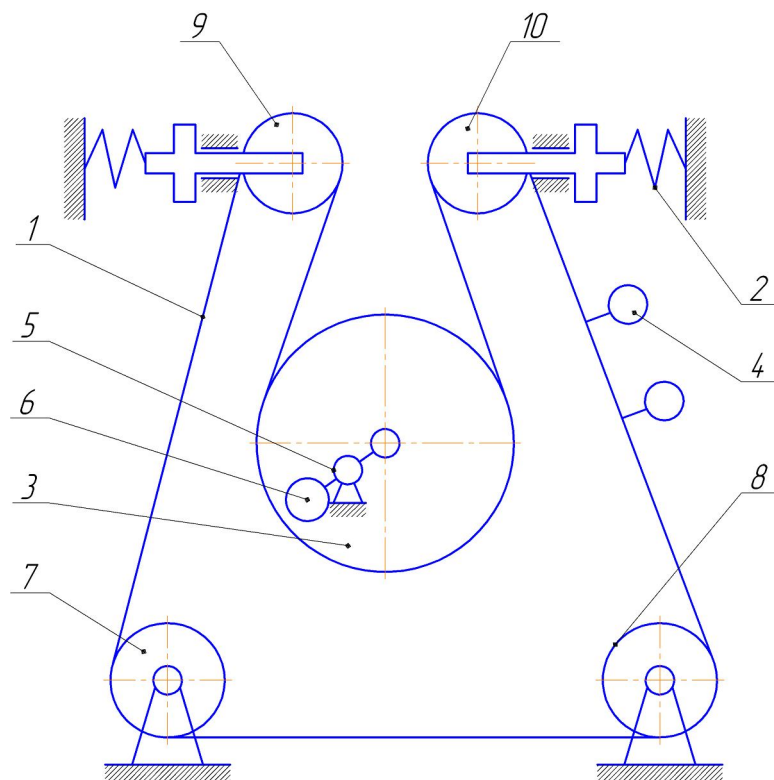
Принципова схема конвеєрної вібраційної машини для обробки деталей в закріпленому стані: 1 транспортерна стрічка; 2 – пружна підвіска; 3 – бічний диск вібробуджувача; 4 – деталь; 5 – приводний вал; 6 – противага; 7,8,9,10 – опорні котки
